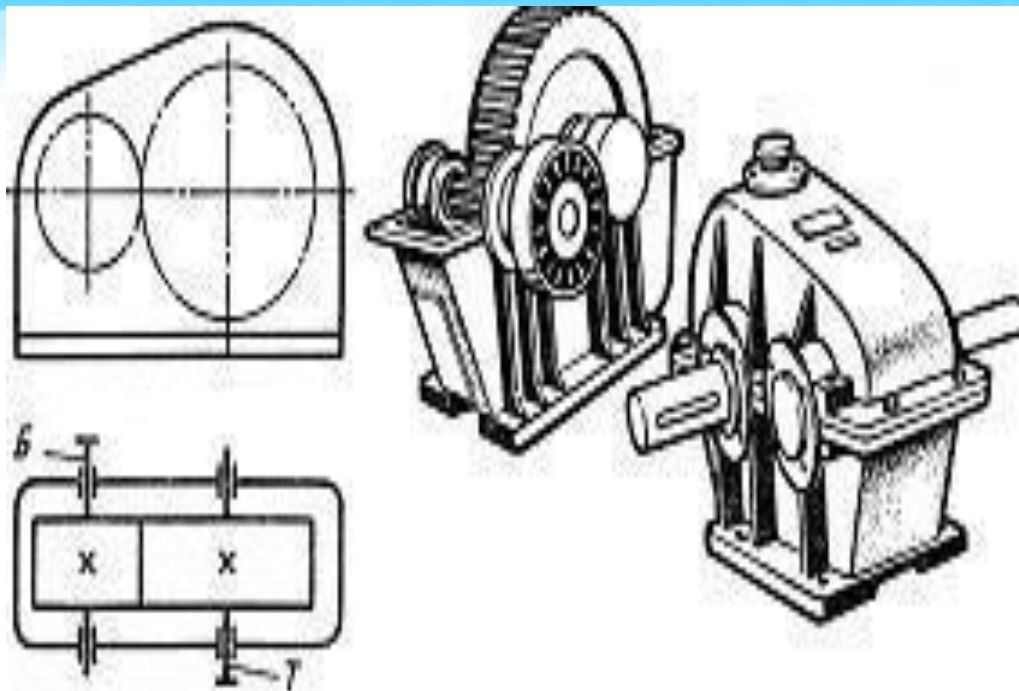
Одноступенчатые цилиндрические редукторы горизонтальные
